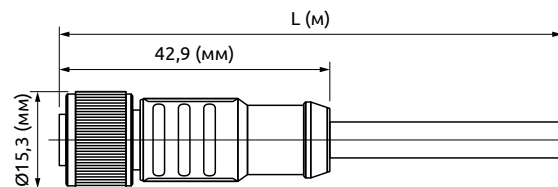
Габаритные размеры кабеля HTE.Cable-M12-6F-xxx
